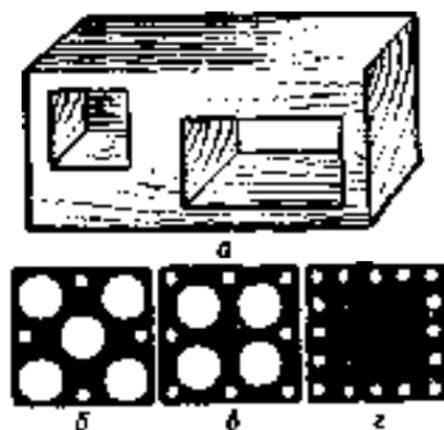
Подготовка глубокого (квадратного) отверстия квадратной формы
